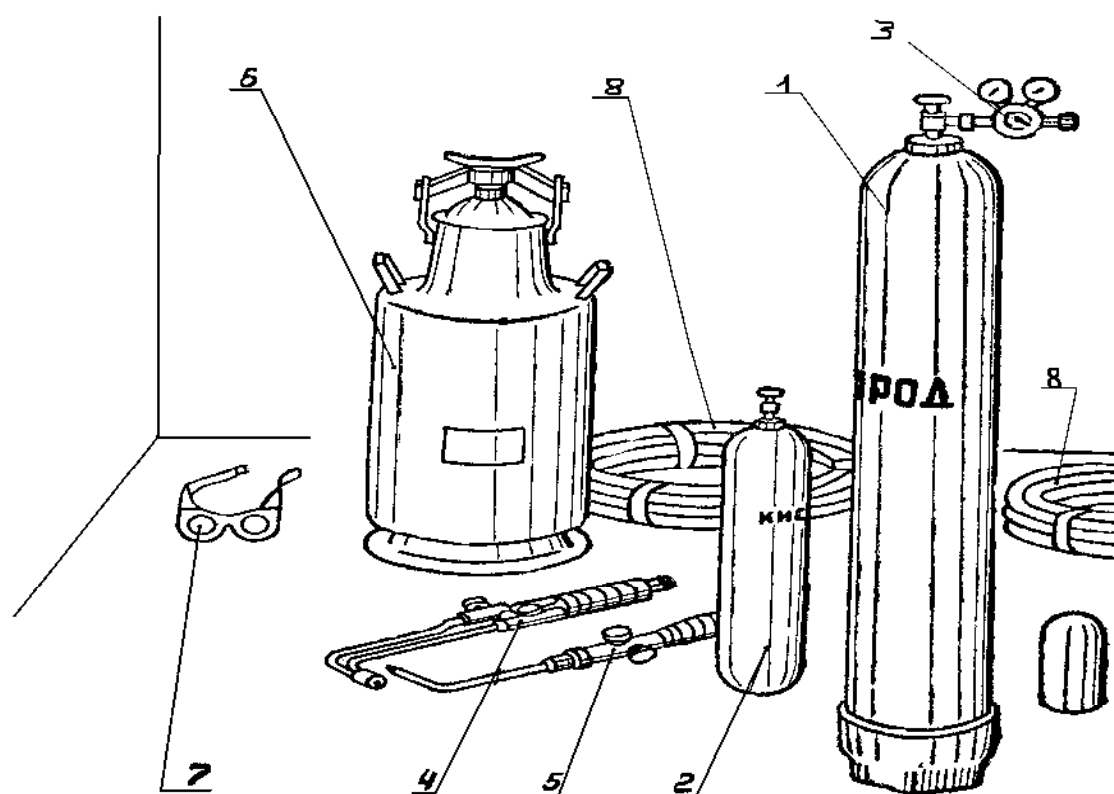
Оборудование для сварки и резки металла:
